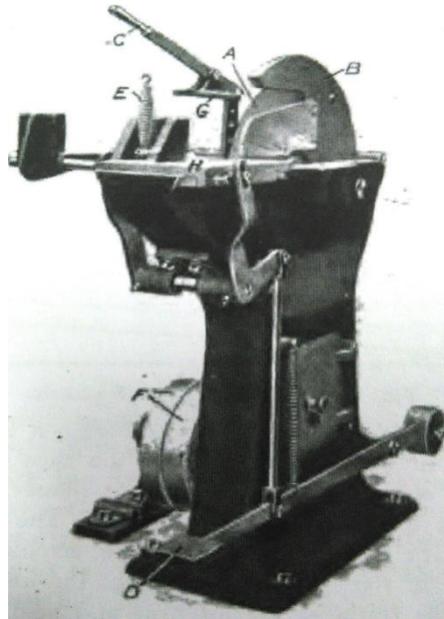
MAQUINA DE CUCHILLO PARA CORTAR EL CAUCHO
